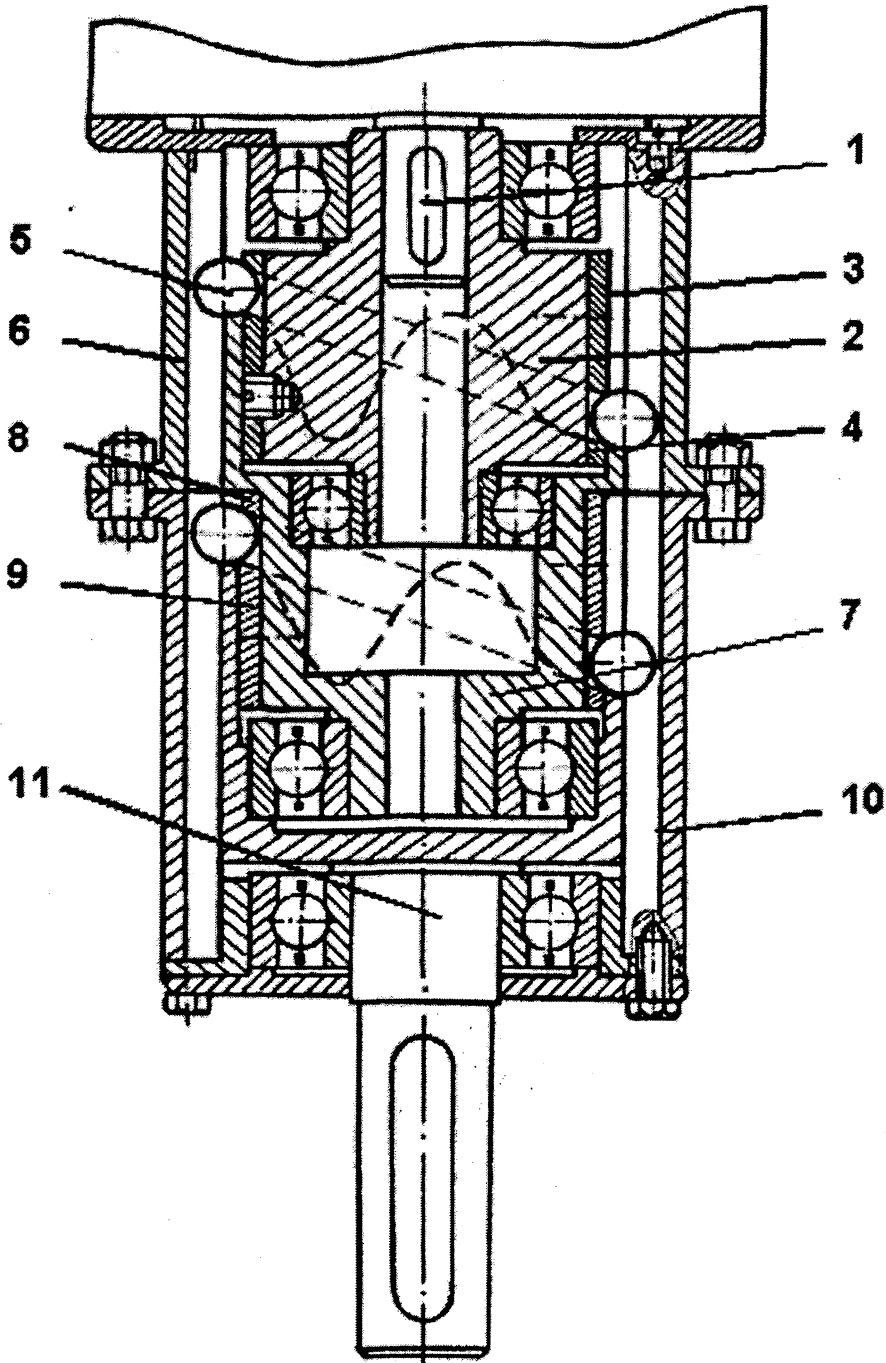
Схема планетарного двухступенчатого шарикового мотор-редуктора
